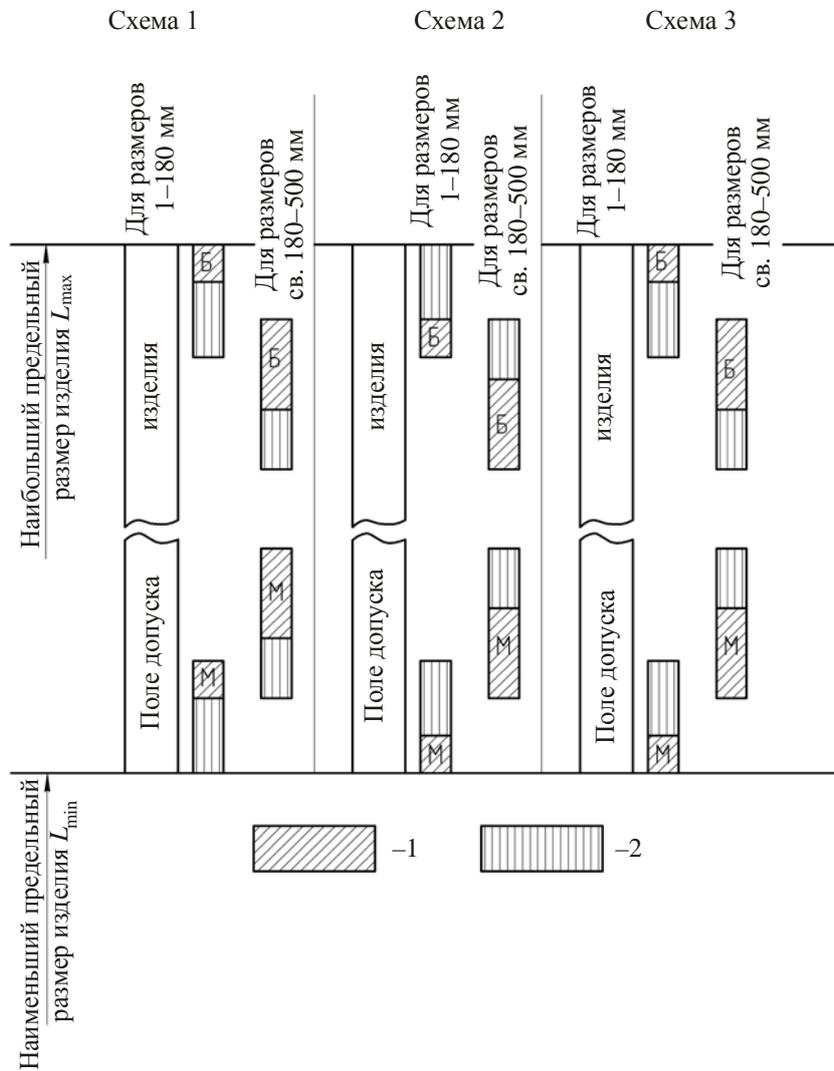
Схемы расположения полей допусков предельных калибров для глубин и высот уступов:
